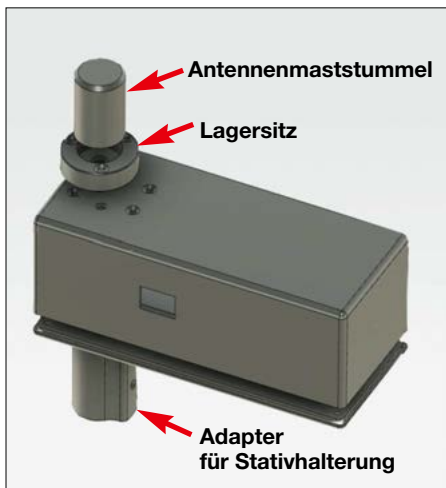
3-D-Ansicht der Gehäuseteile im Druckprogramm
